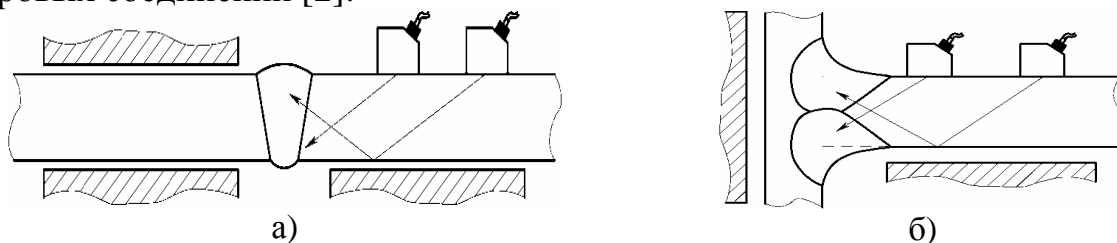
Схемы контроля тавровых и угловых сварных соединений
